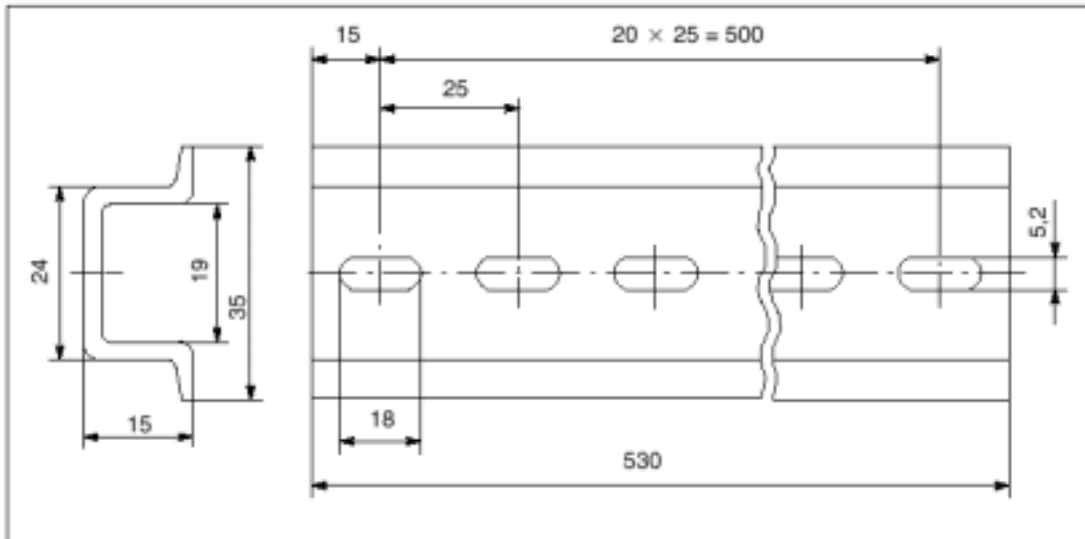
Чертеж с размерами 530-миллиметровой стандартной профильной шины
